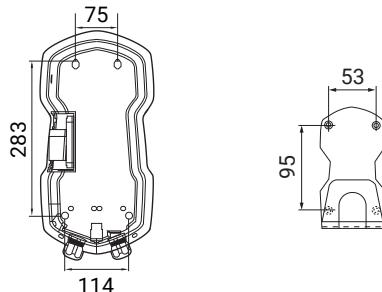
Расположение отверстий для однофазного зарядного устройства
